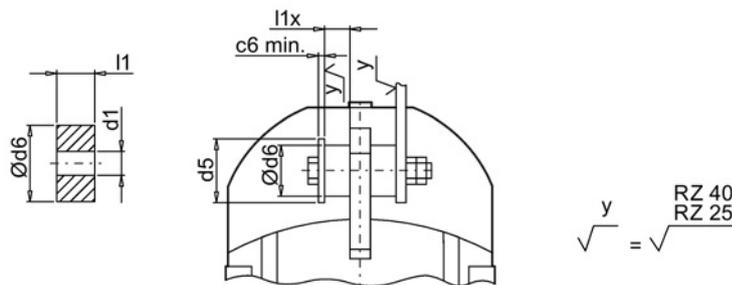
Montagevorschlag für Drehmomentstütze an F.29 - F.149
